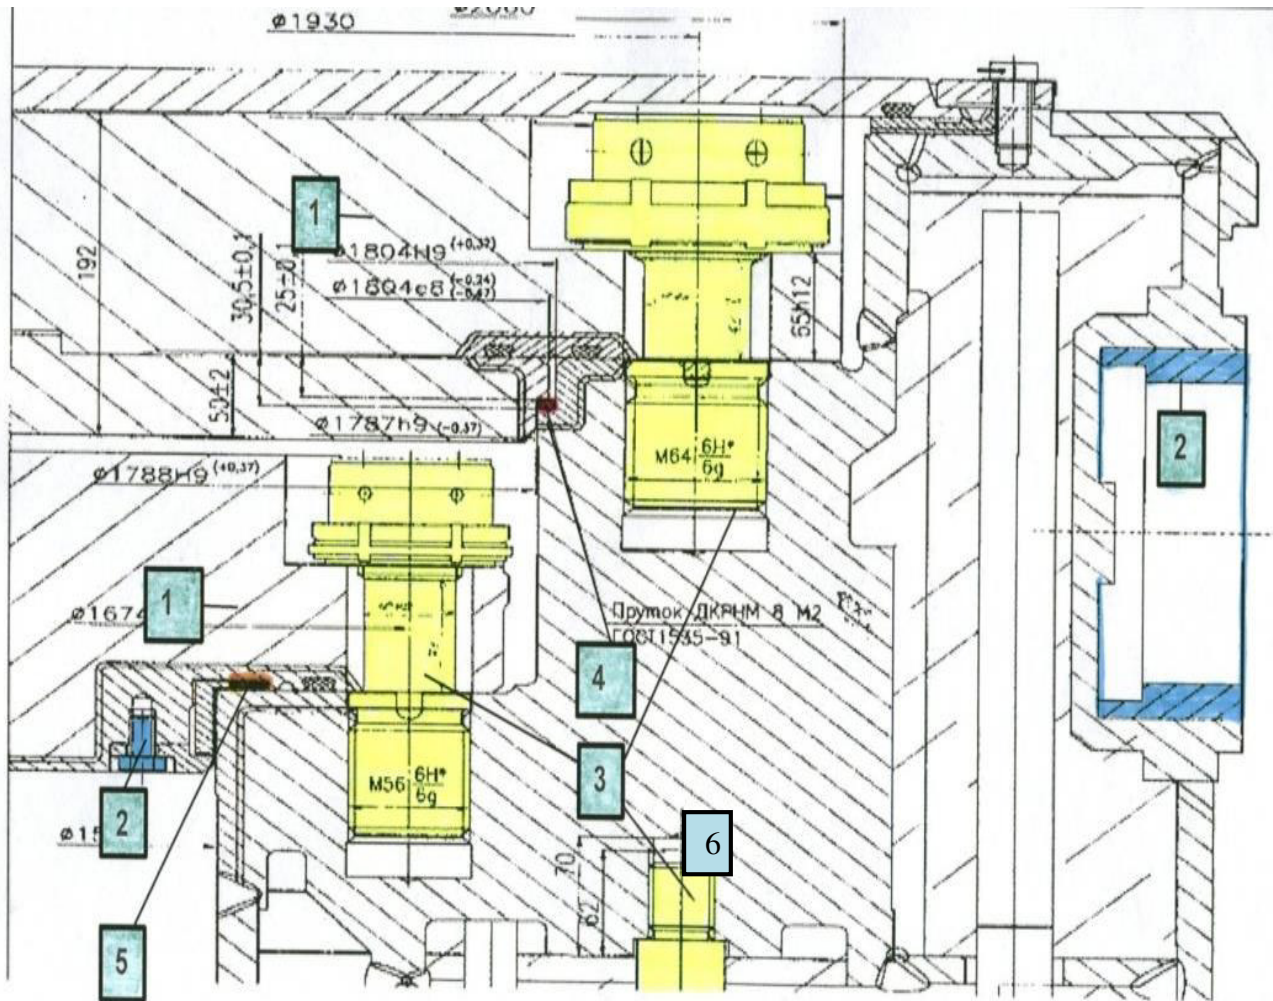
Основные корпусно-крепежные материалы и материалы уплотнения элементов контейнера: 1 – крышка контейнера - сталь марки 08X18H10T; 2 – подцапфная втулка - сталь марки 07X16H4Б; 3 – крепеж - сталь марки 38ХНЗМФА; 4 – прокладка - медь марки М2; 5 – спирально навитое уплотнение, состоящее из вспененного графита + стали марки 12X18H10T, 6 – корпус контейнера - сталь марки 09Г2СА-А
